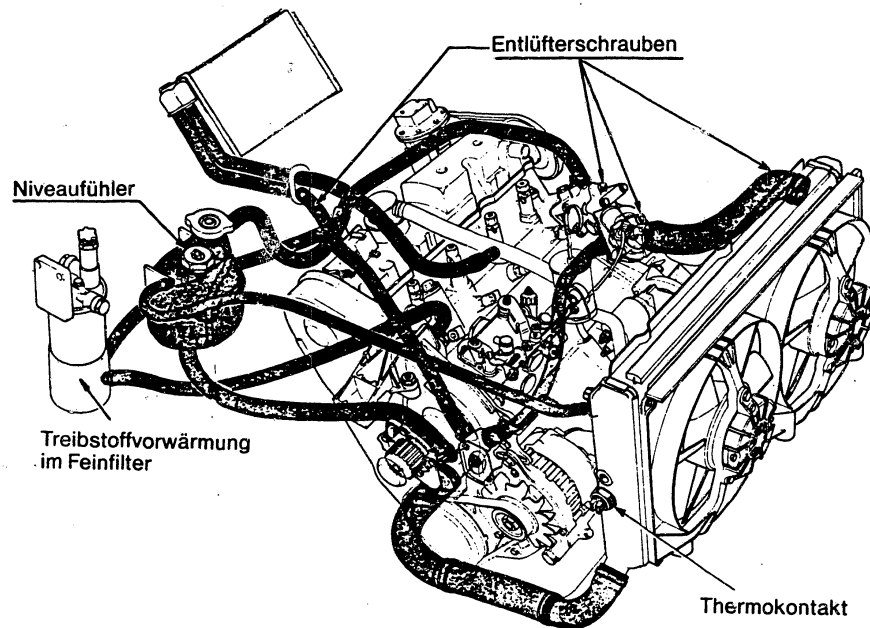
Zum Entlüften des Kühlsystems sind alle drei Entlüfterschrauben zu öffnen und der Ausgleichsbehälter bis zum Rand mit Kühlflüssigkeit zu füllen. Die Entlüfterschrauben sind zu schliessen, sobald die Flüssigkeit blasenfrei austritt.
